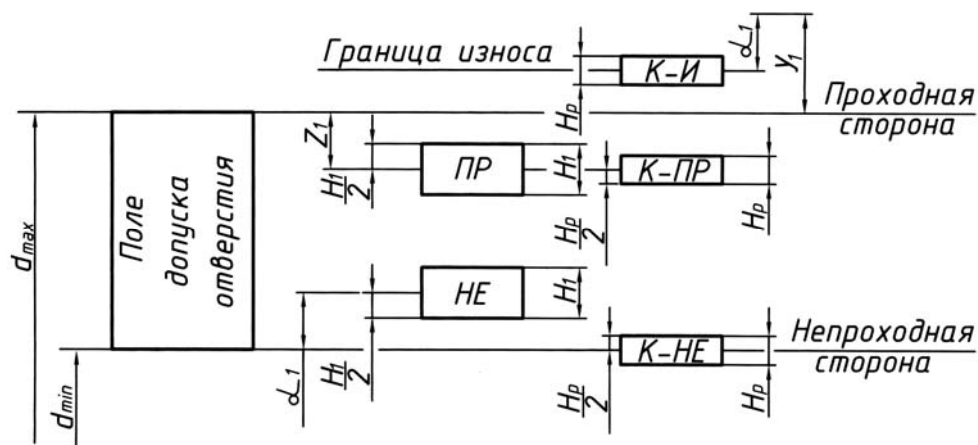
Схема полей допусков калибр-скобы для размеров свыше 180 мм
